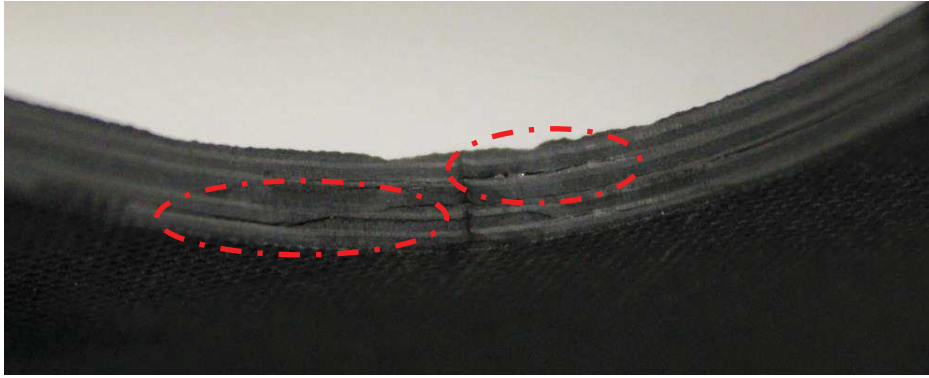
Etat de surface après découpe, au niveau du défaut généré par l'arrêt brutal de la machine
